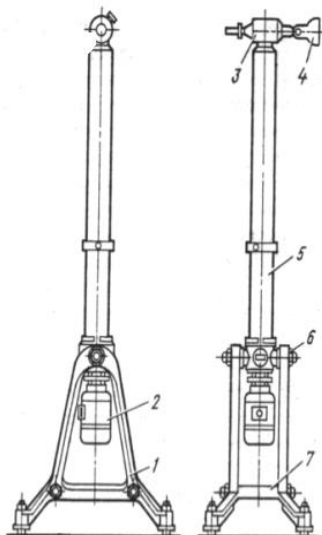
Электромеханический краскораспылитель: 1 - стойка станины; 2 - привод электромеханический; 3 - головка; 4 - насадка; 5 - стойка; 6 - зажимное устройство; 7 - стяжка станины
